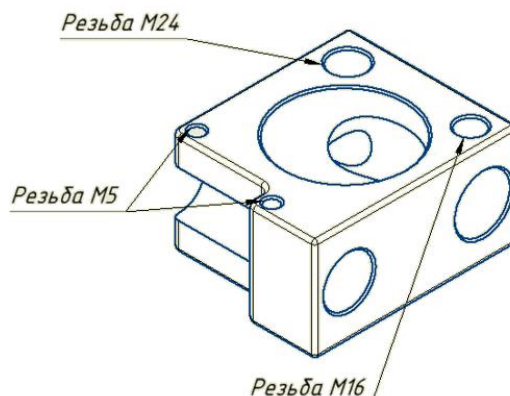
Корпусная деталь с различными резьбовыми отверстиями
